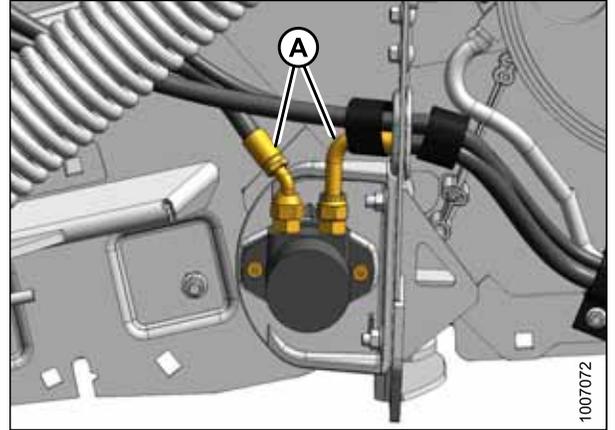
Motor hidráulico trasero; lado izquierdo
